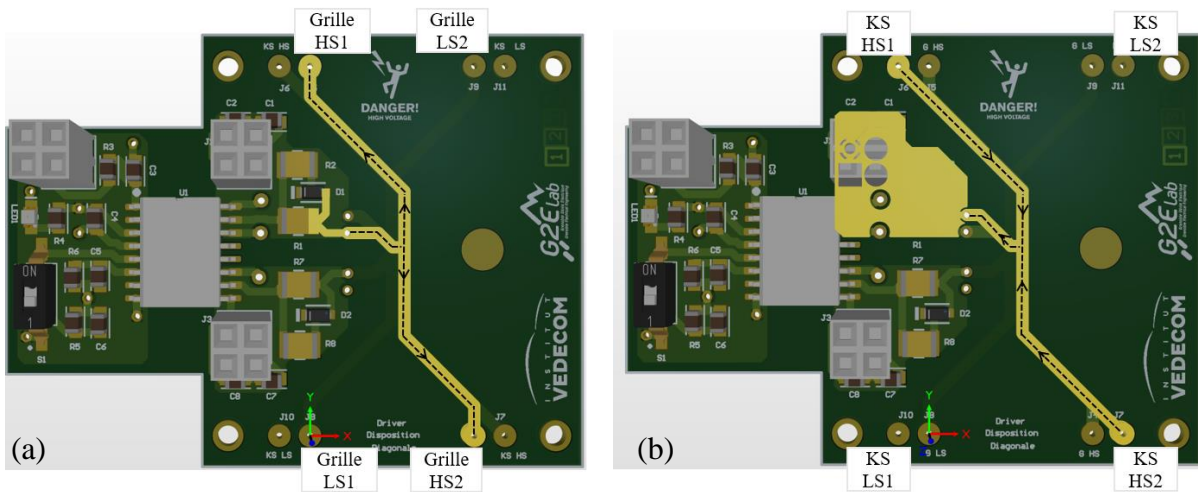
Driver du module PN_2PCB à design non croisé (a) Couche supérieure (b) Couche interne
